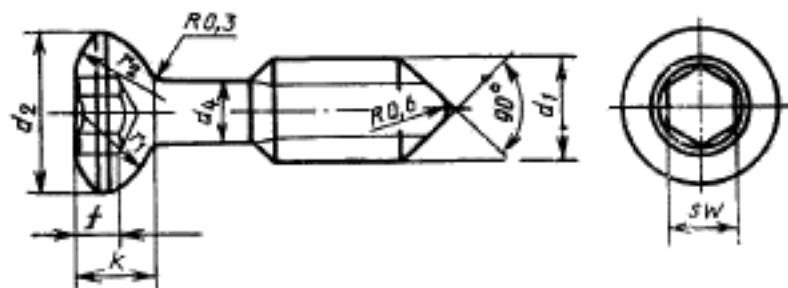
Шуруп с глубокой резьбой (НВ)
